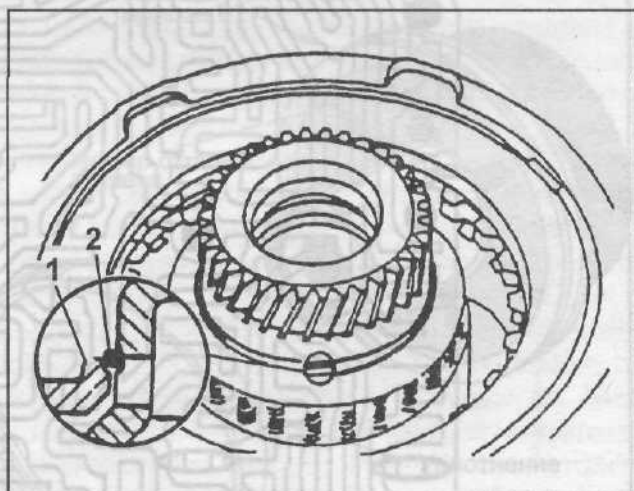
1 - Шайба; 2 - Стопорное кольцо.
